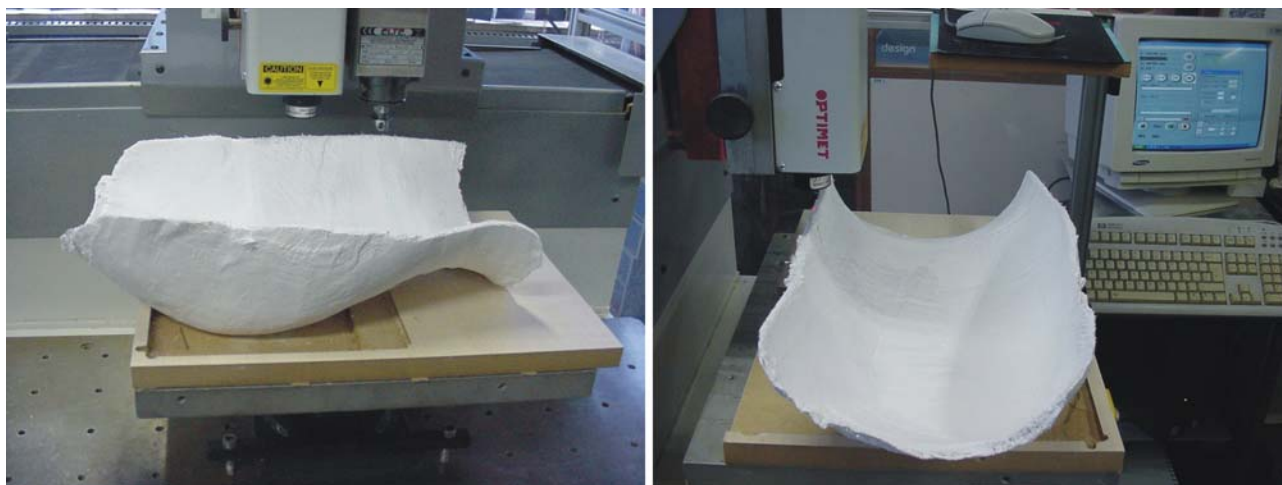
Molde de Gesso (encosto do assento) a ser digitalizado no Scanner Tridimensional a Laser modelo Digimill 3D, em vista lateral (A) e em vista superior (B).
